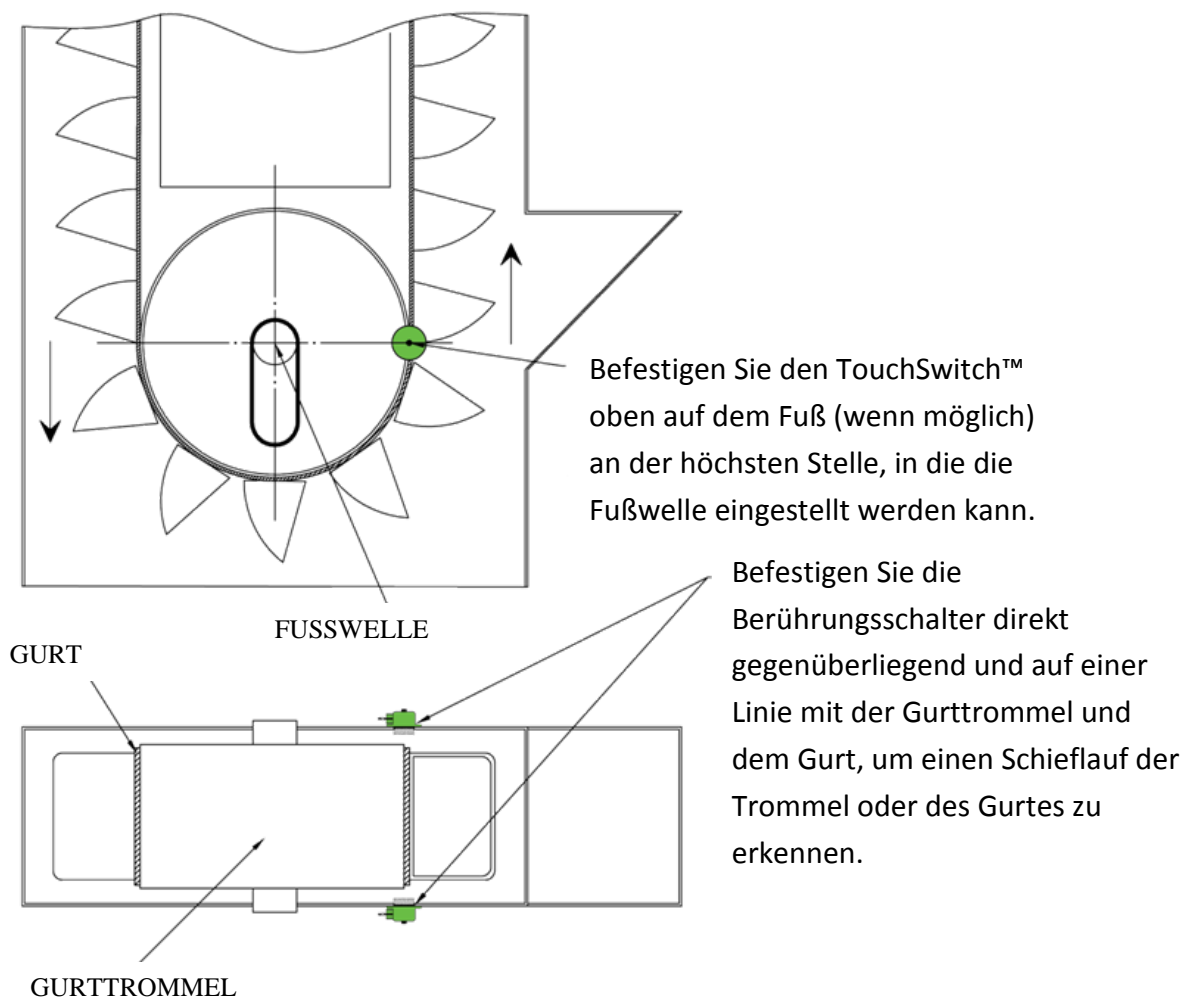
Touchswitch™ Montageposition – Untere Umlenktrummel
